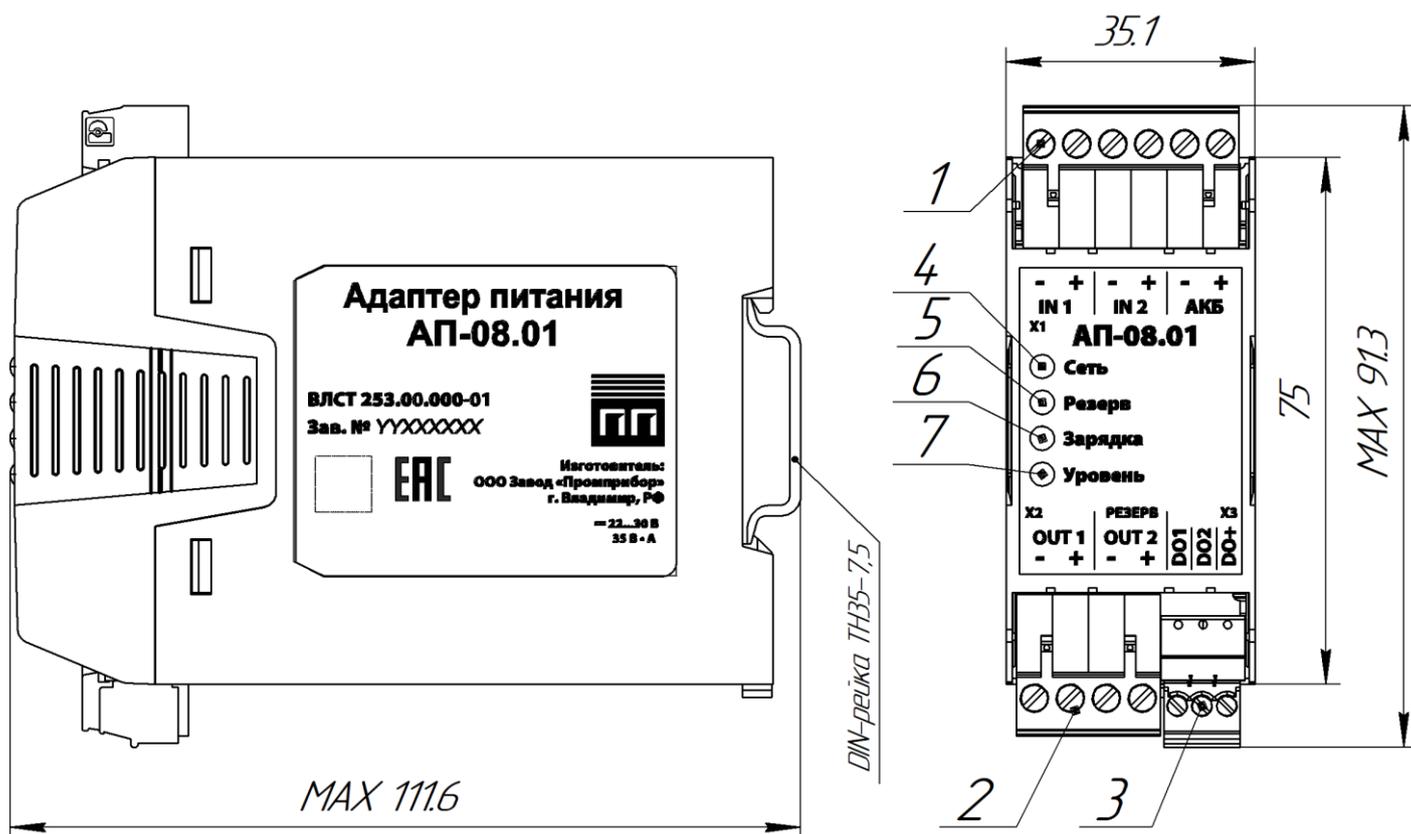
Внешний вид и размеры адаптера АП-08.01
